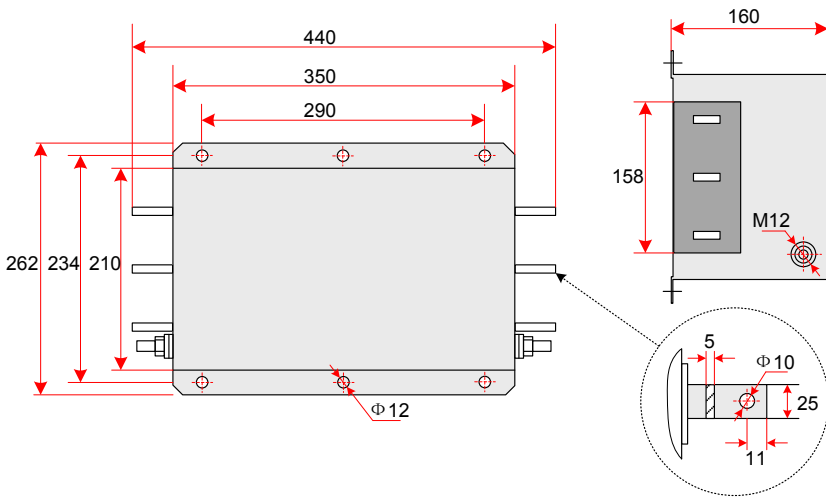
坚力滤波器 250A 尺寸图 (单位: mm)
